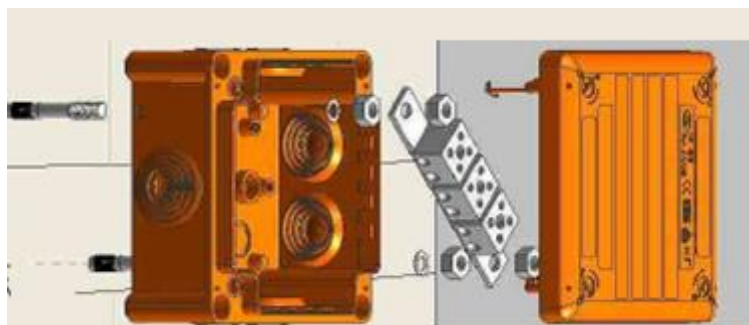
Схема монтажа коробки огнестойкой на бетонное основание
